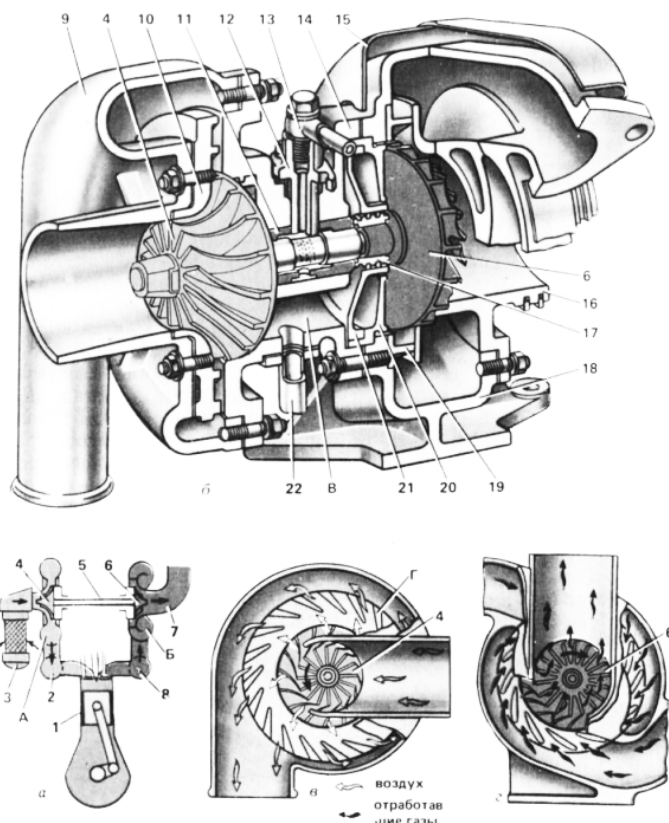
Турбокомпрессор дизеля СМД-62: а — принципиальная схема турбонаддува, б — устройство турбокомпрессора, в — поток воздуха в компрессоре; г — поток выпускных газов в турбине; 1 — дизель; 2 — впускной коллектор; 3 — воздухоочиститель; 4 — колесо компрессора; 5 — вал; 6 — колесо турбины; 7 — выпускная труба; 8 — выпускной коллектор; 9 — корпус компрессора; 10 — вставка компрессора; 11 — подшипник (плавающая втулка); 12 — фиксатор подшипника; 13 — трубка подвода масла; 14 — средний корпус; 15 — кожух турбины; 16 — вставка турбины; 17 втулка уплотнения турбины; 18 — корпус турбины; 19 — сопловый венец; 20 экран; 21 — диск уплотнения турбины; 22 — трубка слива масла
